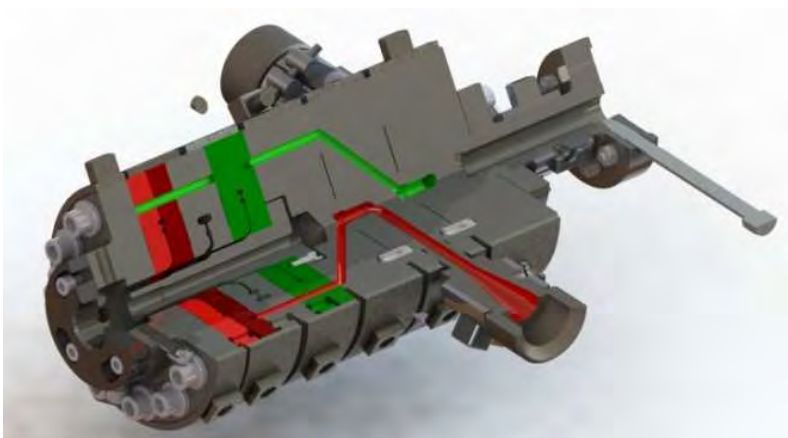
Dreischicht Coextrusionswerkzeug für Medizintechnik
